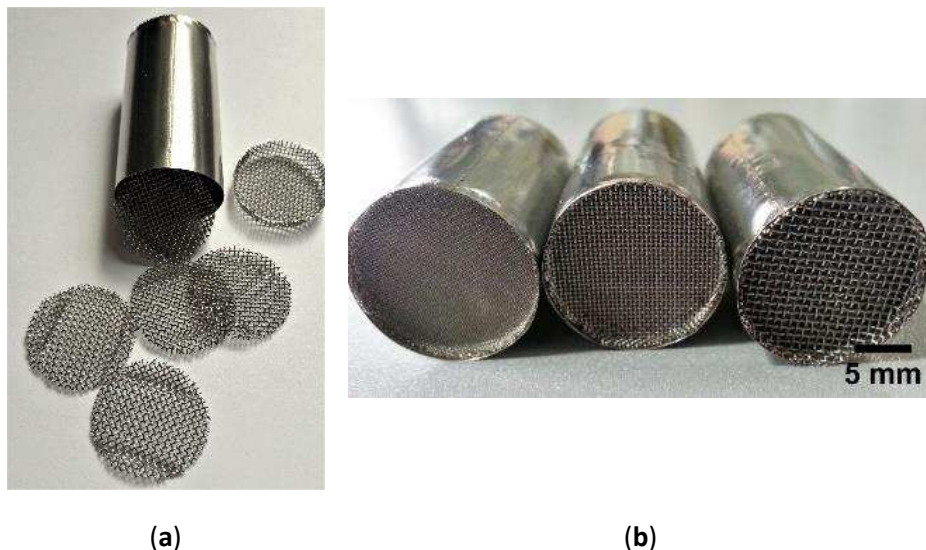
Monolitos de mallas metálicas: (a) mallas internas con dos canales transversales, (b) monolitos metálicos con distintos tipos de mallas metálicas.
